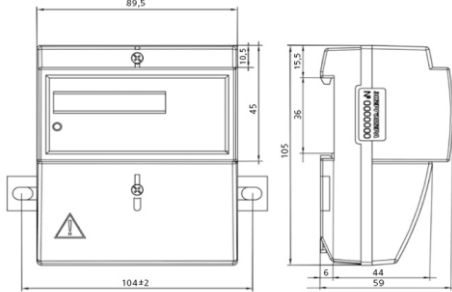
Загальний вигляд лічильника ЦЭ6807Б-У в корпусі P5.1
